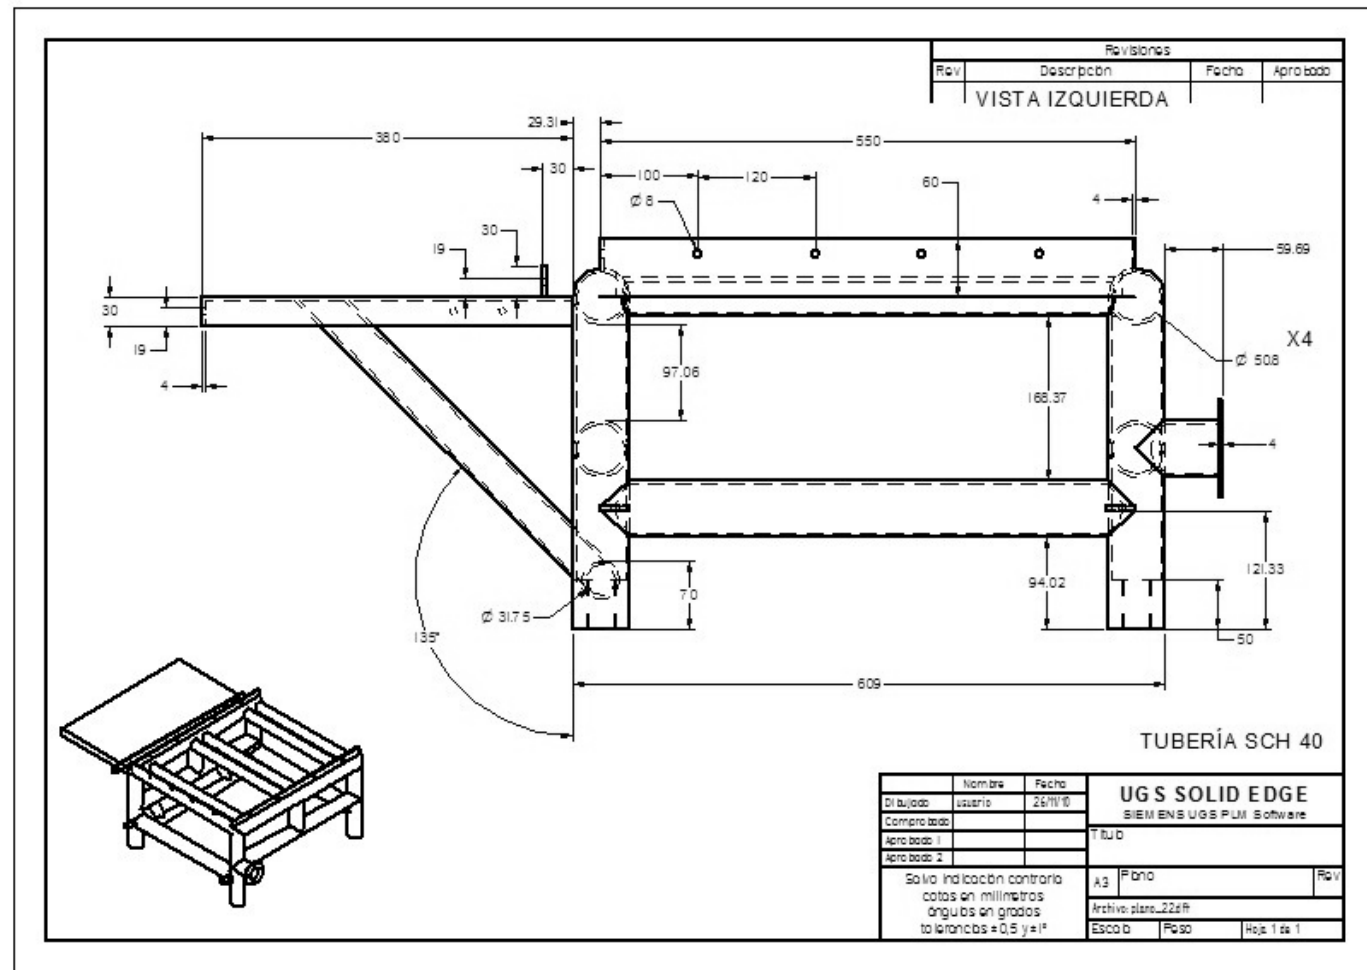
Plano de soporte de moto-reductor, vista frontal.
